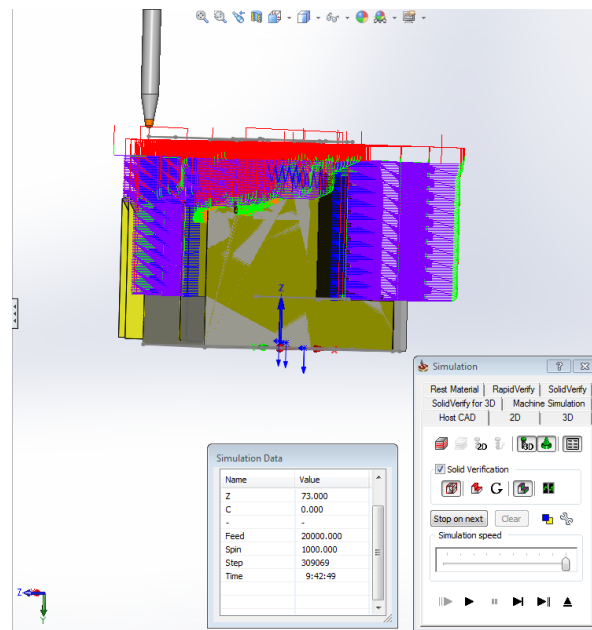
Tool Endmill*  $\varnothing 16\text{mm}$  Untuk Proses CNC *Roughing*.
